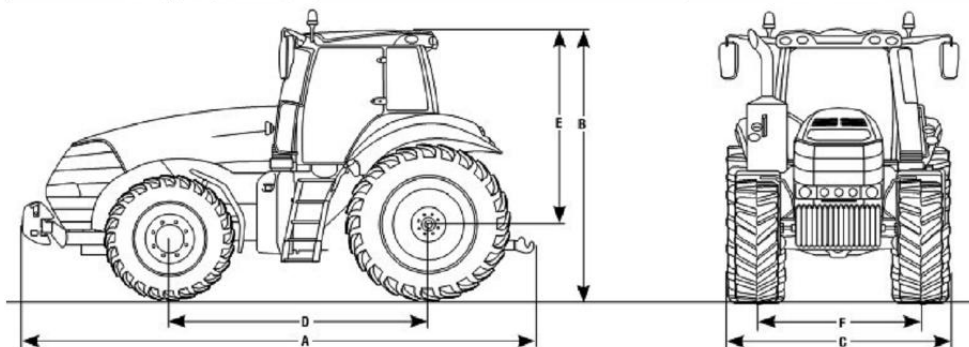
Dimensioni di trattore gommato di grandi dimensioni.
